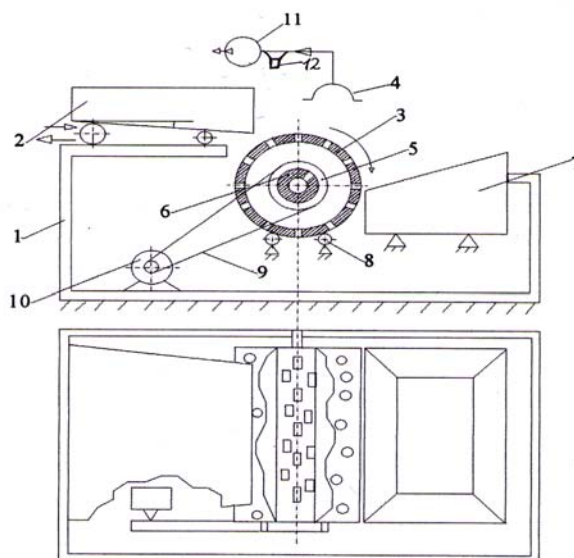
Схема роторного сепаратора для отделения легковесных примесей: 1 – рама; 2 – подающий лоток; 3 – роторный барабан; 4 – аспирационный канал; 5 – приводной шкив; 6 – воздушный распределитель; 7 – бункер очищенных семян; 8 – опорный ролик; 9 – привод ротора; 10 – электродвигатель; 11 – вакуум – насос; 12 – циклон-пылесборник
